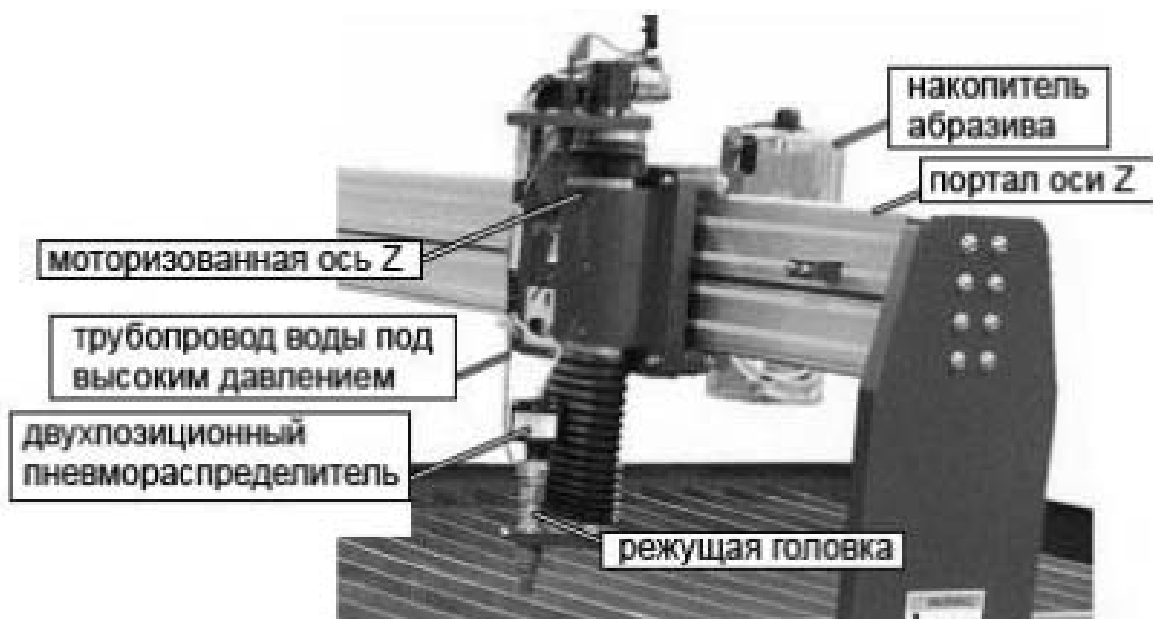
Ось Z установки MAXIEM и компоненты режущей головки
